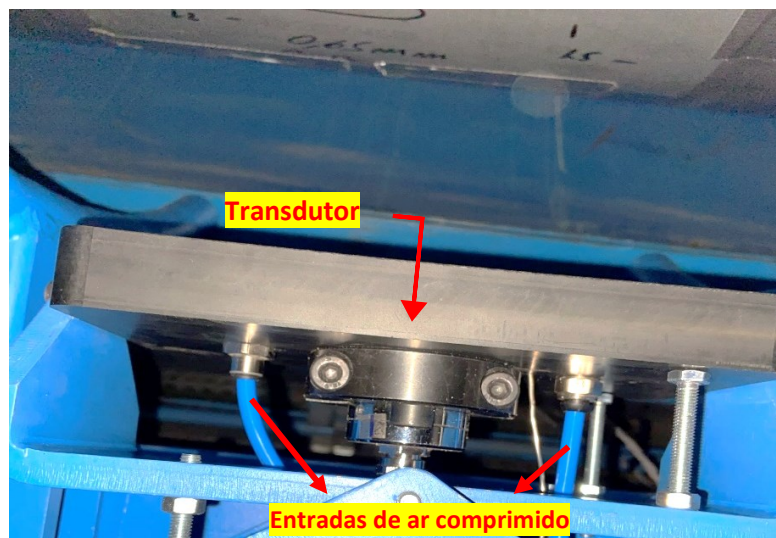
Configuração do suporte de fixação do transdutor – Montagem.
